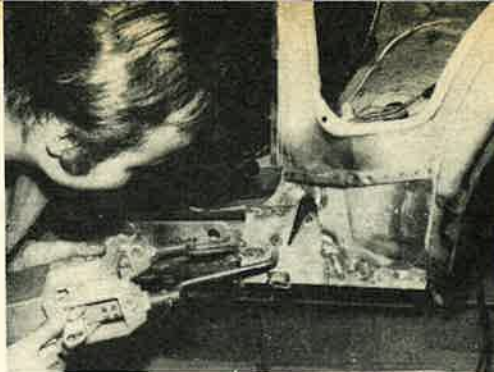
Soudage par résistance gousset renfort latéral gauche sur longeron. Pince ARO 169 A (photo R.T.C.).
